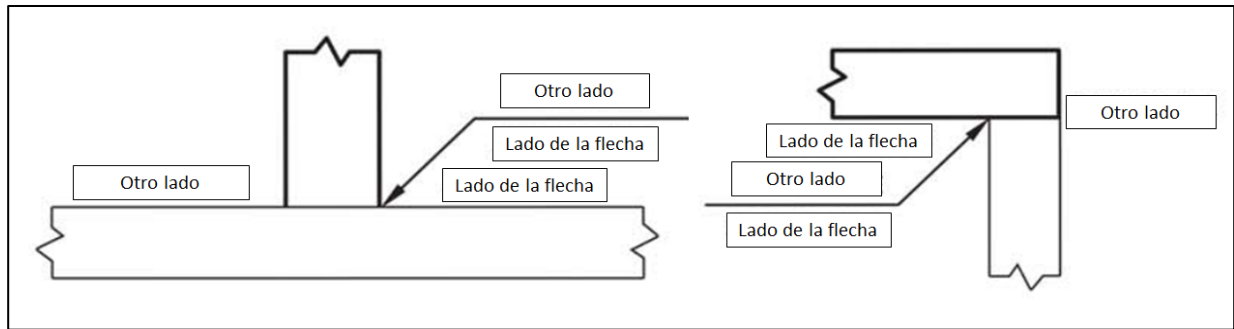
Lados De La Flecha Para Indicar El Lado Donde Debe Realizarse Una Soldadura [85].
